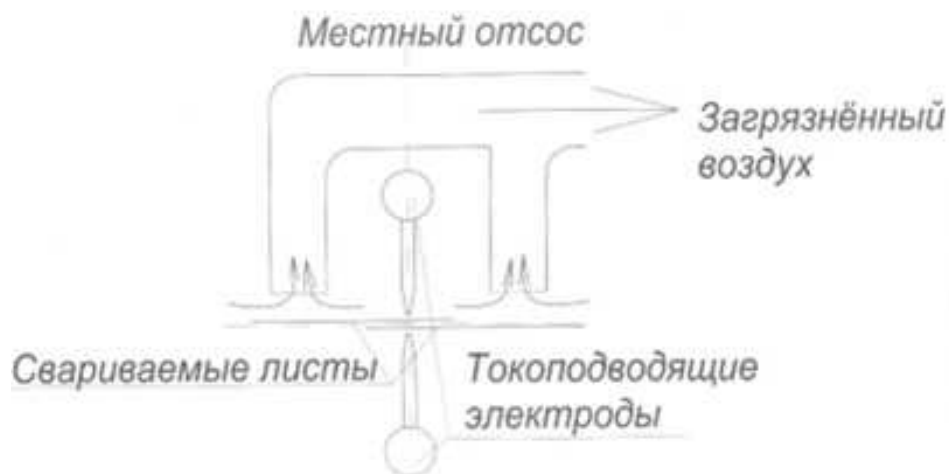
Схема вентиляции мест точечной сварки
